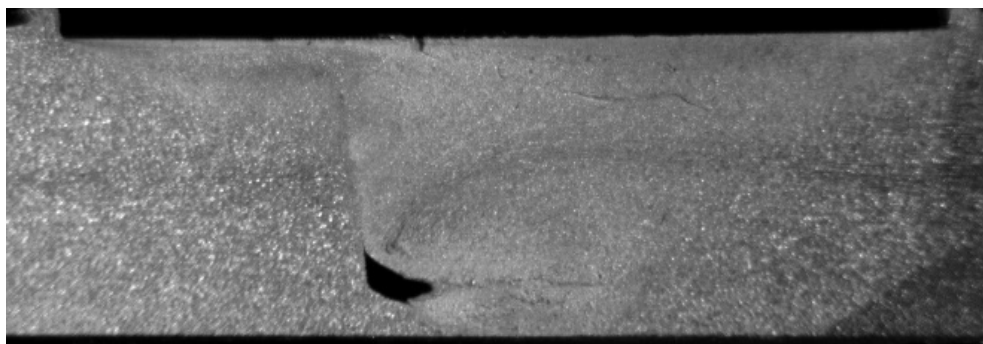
Макрошлиф сварного соединения при угле наклона инструмента к вертикали 0°
